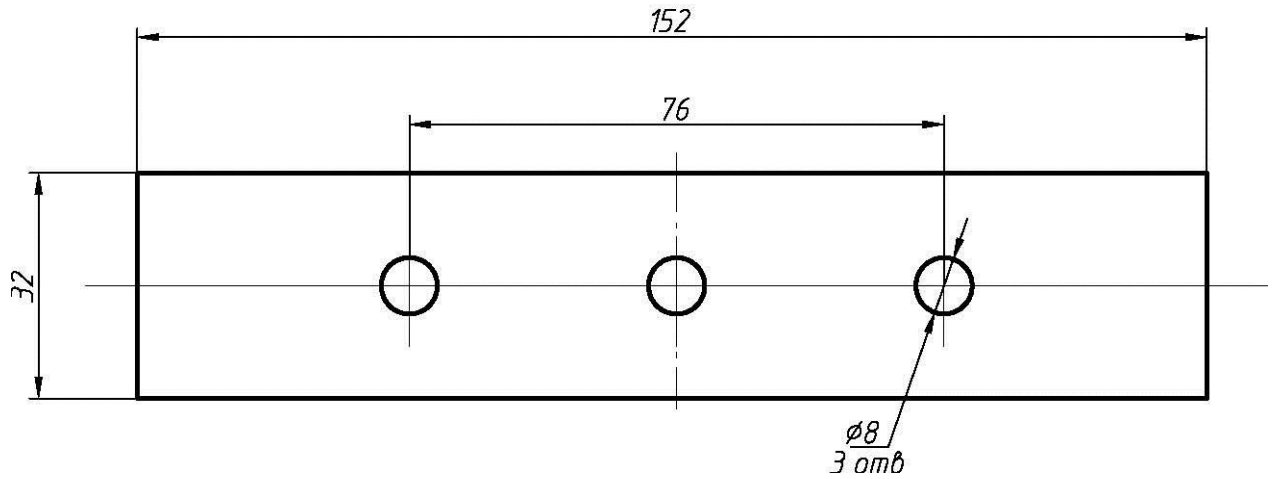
Присоединительные размеры скобы Оповещателя РУПОР-В
